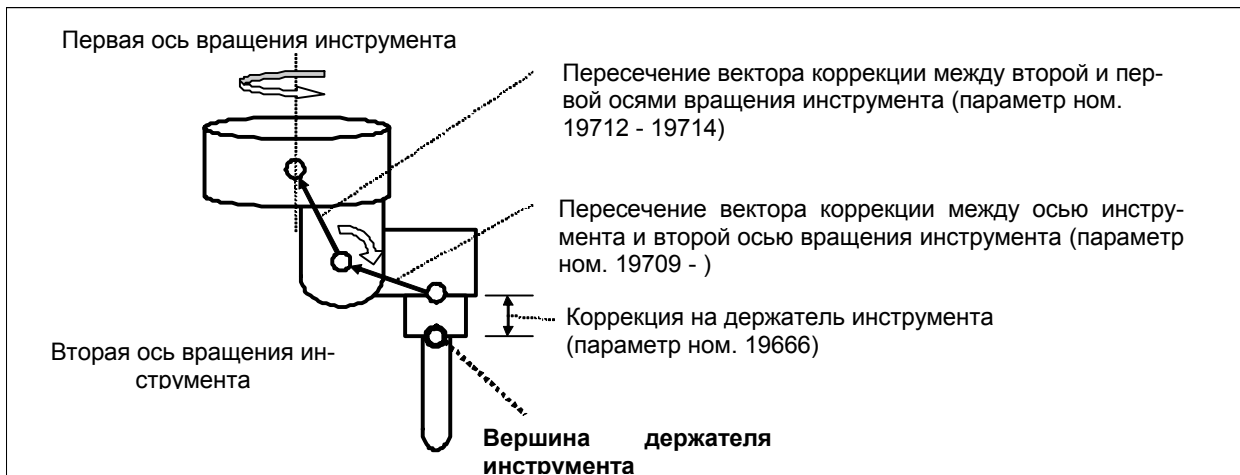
(h) Определение позиции вершины держателя инструмента
